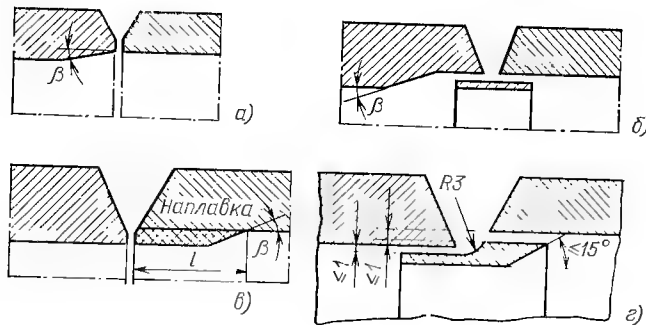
Способы подготовки кромок при стыковке труб с разными внутренними диаметрами.
